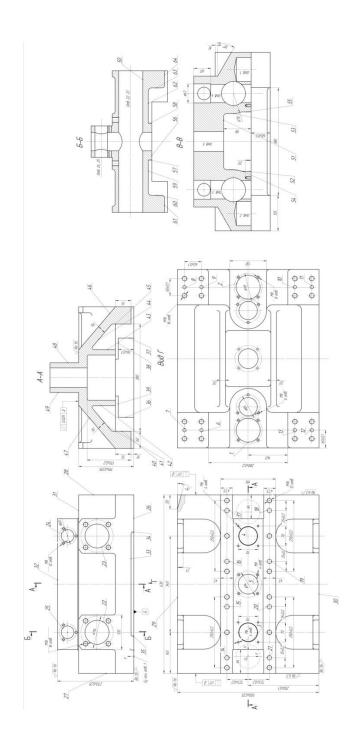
Общий вид детали - «Корпус приспособления»
